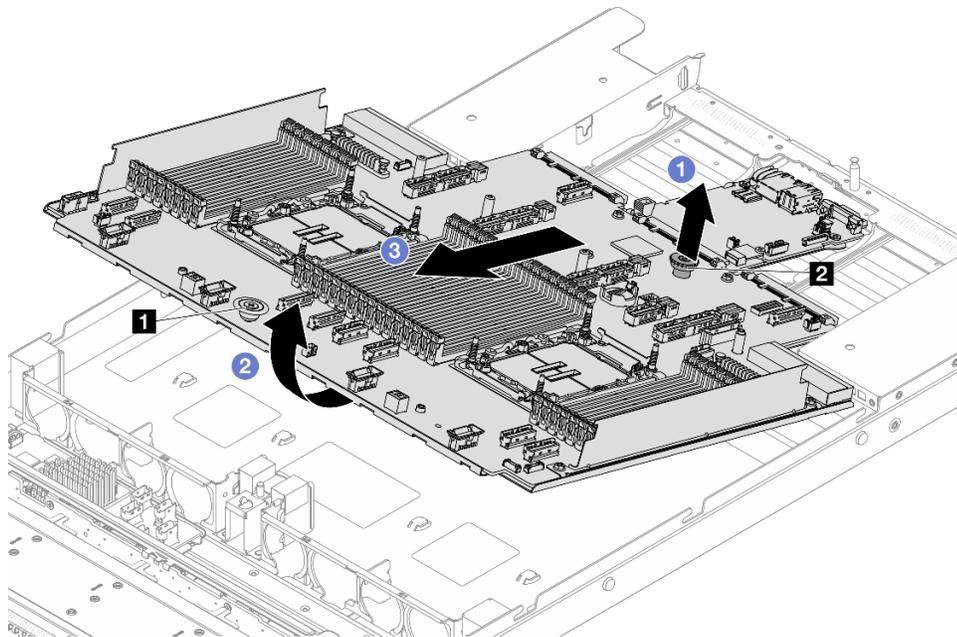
Entfernen der Systemplatinenbaugruppe
